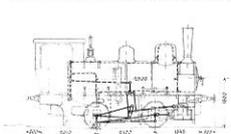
2 C 2-Schweizerische Hauptbahn-Lokomotive, gebaut von der Maschinenfabrik Norddeutscher Lloyd in Hamburg.
